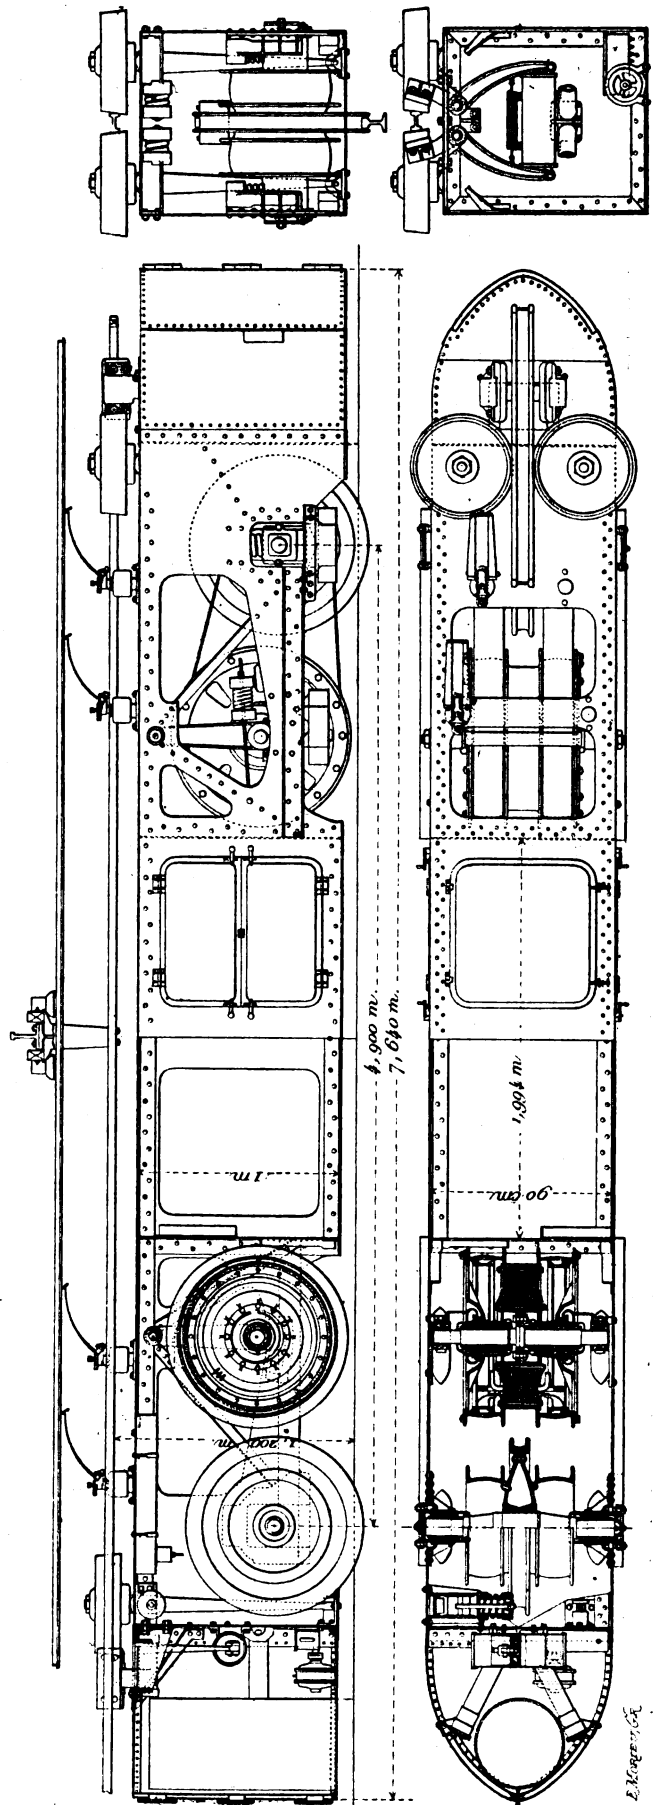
Coupe longitudinale, élévation et plan du véhicule automoteur.
